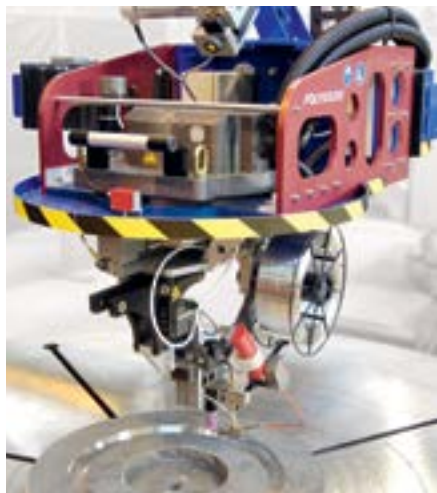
Установка для наплавки корпуса клапана вытянутой формы, которые применяются в нефтеперерабатывающей промышленности. Сварочная головка позиционируется двумя суппортами, установленными на кронштейне консольной балки. Траектория движения горелки состоит из вращательных движений на 180° вокруг сварочной головки и из перемещения вдоль суппорта. Применение коллекторной головки позволяет выполнять непрерывную наплавку, т.к. нет необходимости наматывать кабели и шланги.
